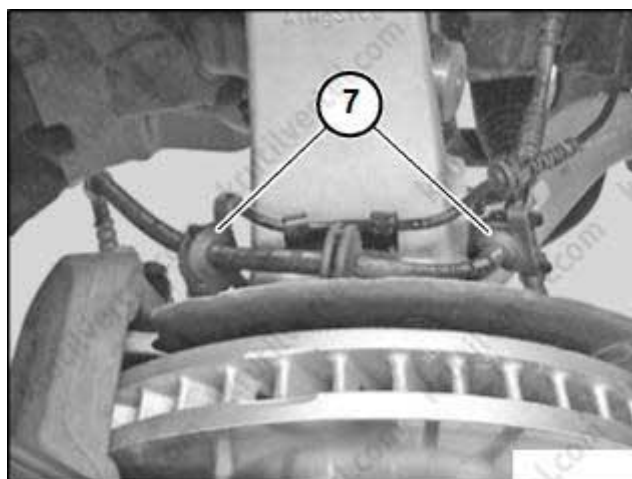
Демонтаж шлангу з кріплень:
